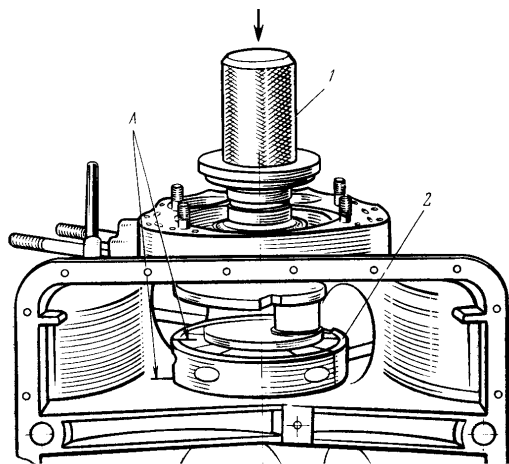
Запрессовка средней опоры коленчатого вала: 1 — оправка; 2 - средняя опора; А — метки на средней опоре и картере коленчатого вала для совмещения масляных каналов
